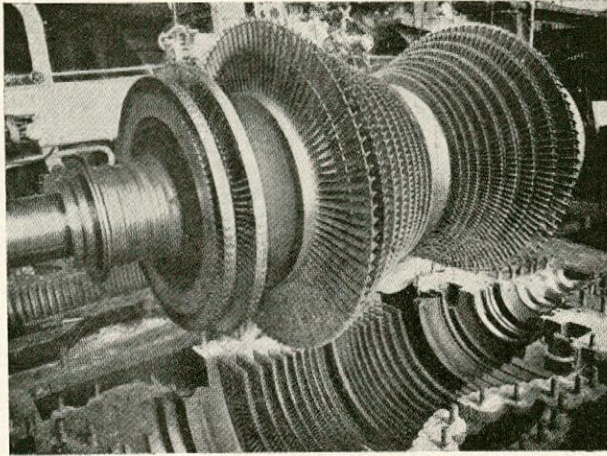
Destruyores "Daring". Rotor de B. P. Pametrada.
